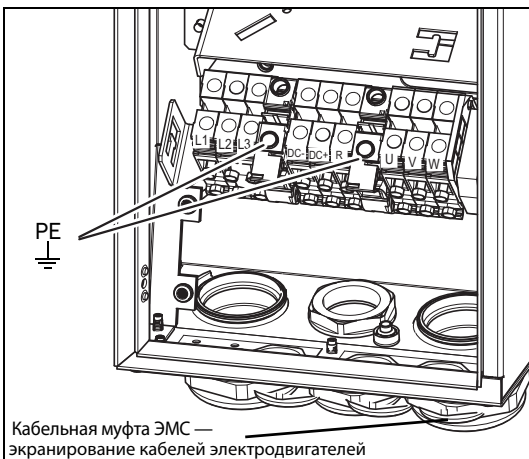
Подключение сетевого питания и двигателя модели 002-025, размер корпуса С69
